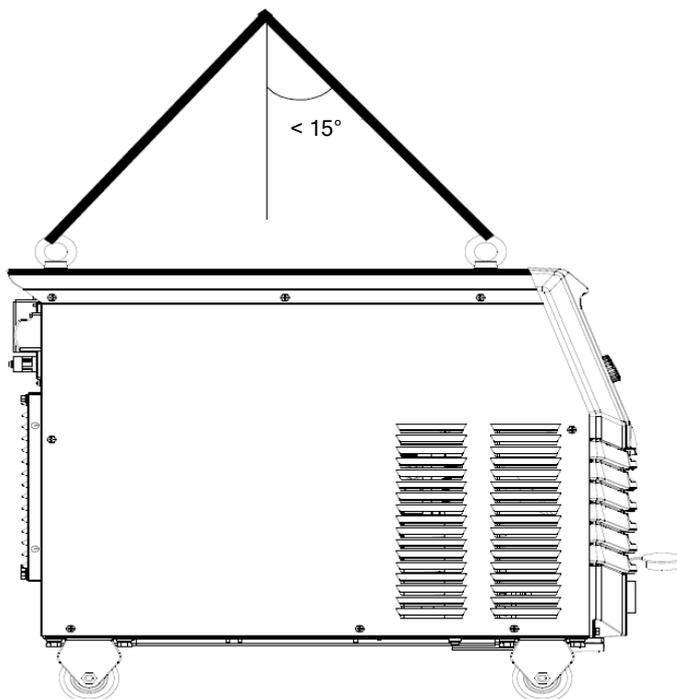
Схема перемещения сварочного аппарата с помощью подъемного крана
